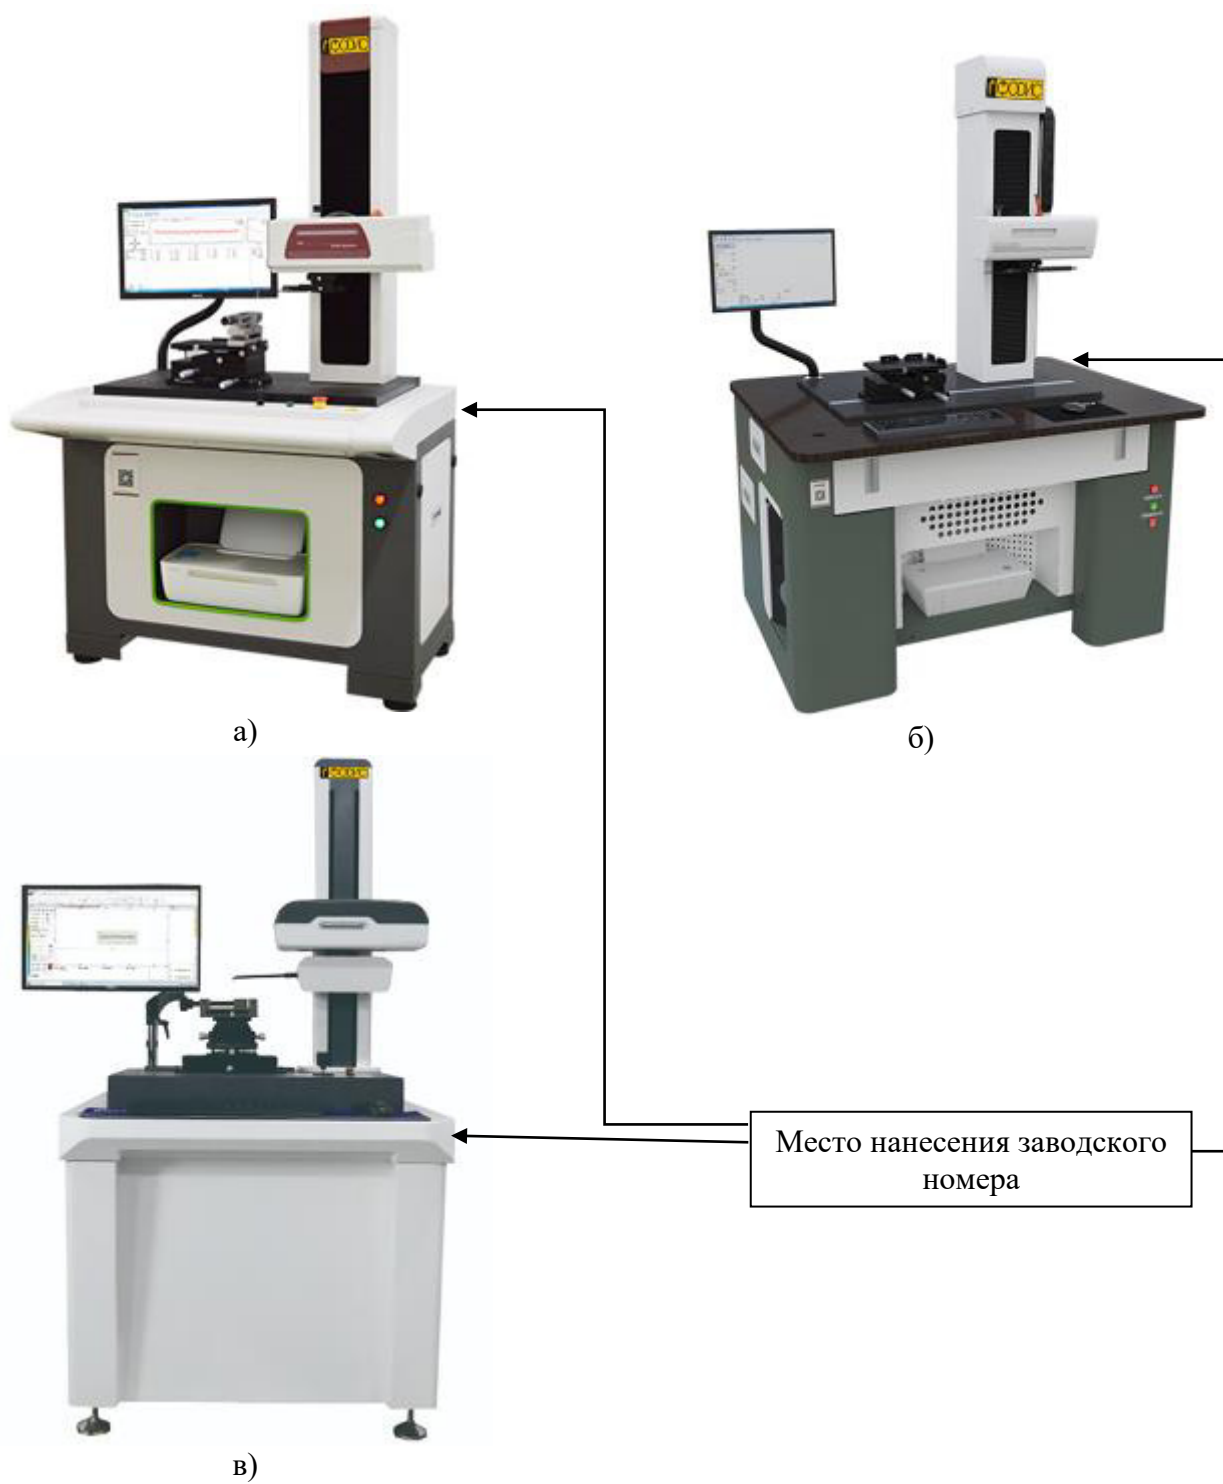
Общий вид приборов для измерений параметров шероховатости поверхности Fodis а) SR1000; б) SR2000; в) SR3000
